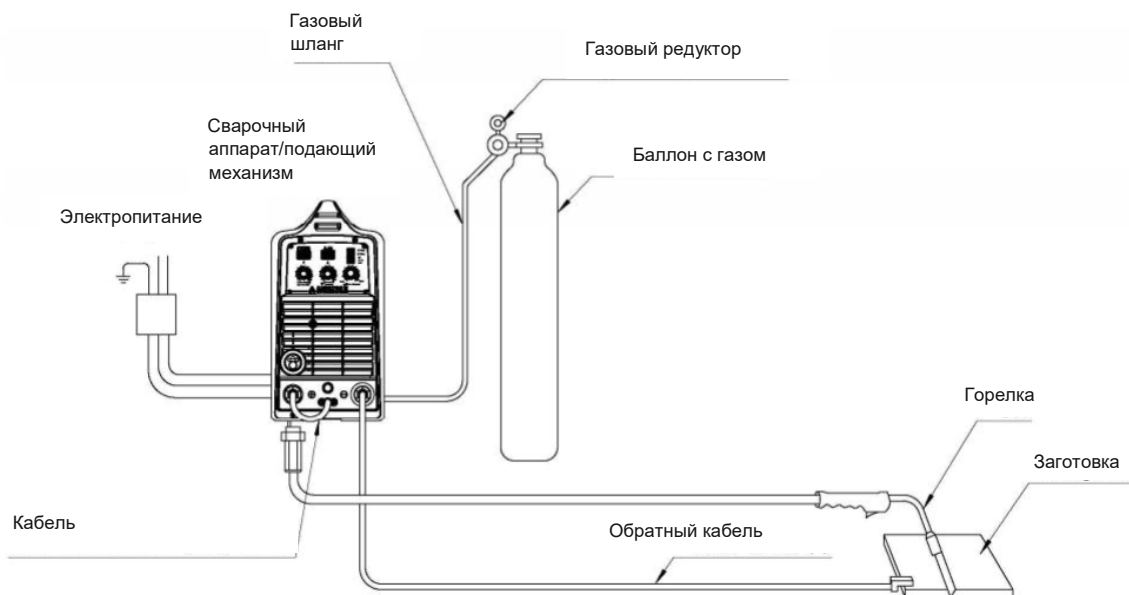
MIG/MAG сварка проволокой из углеродистой стали с помощью проволочной горелки толкающего типа
